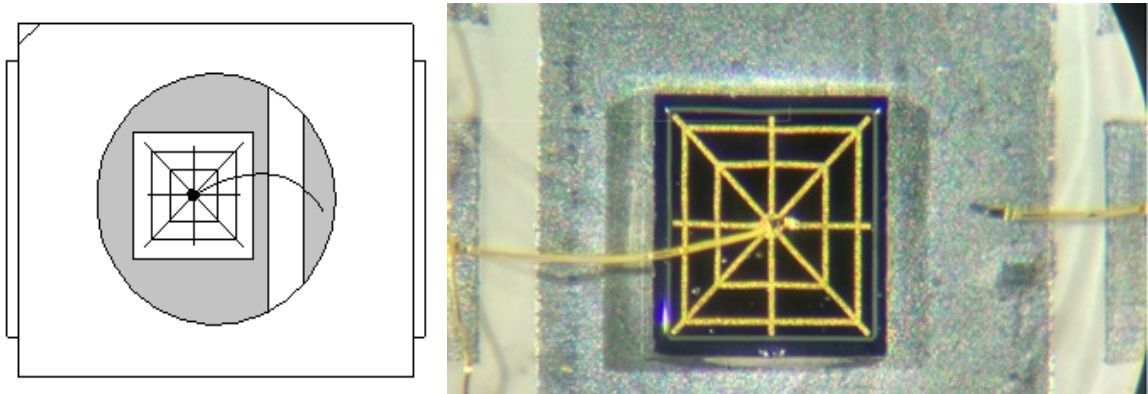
Кристалл фотодиода, разваренный в корпусе SMD 3528
